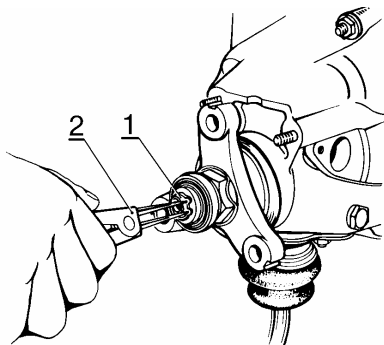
Снятие стопорного кольца с конца вторичного вала:
